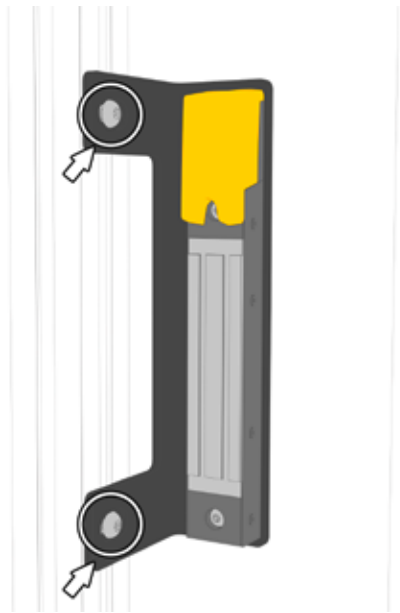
Montageplatte mit Prozesszuhalterung am Profil anbringen und und Schrauben M8 x 12 mm Torx festziehen.
